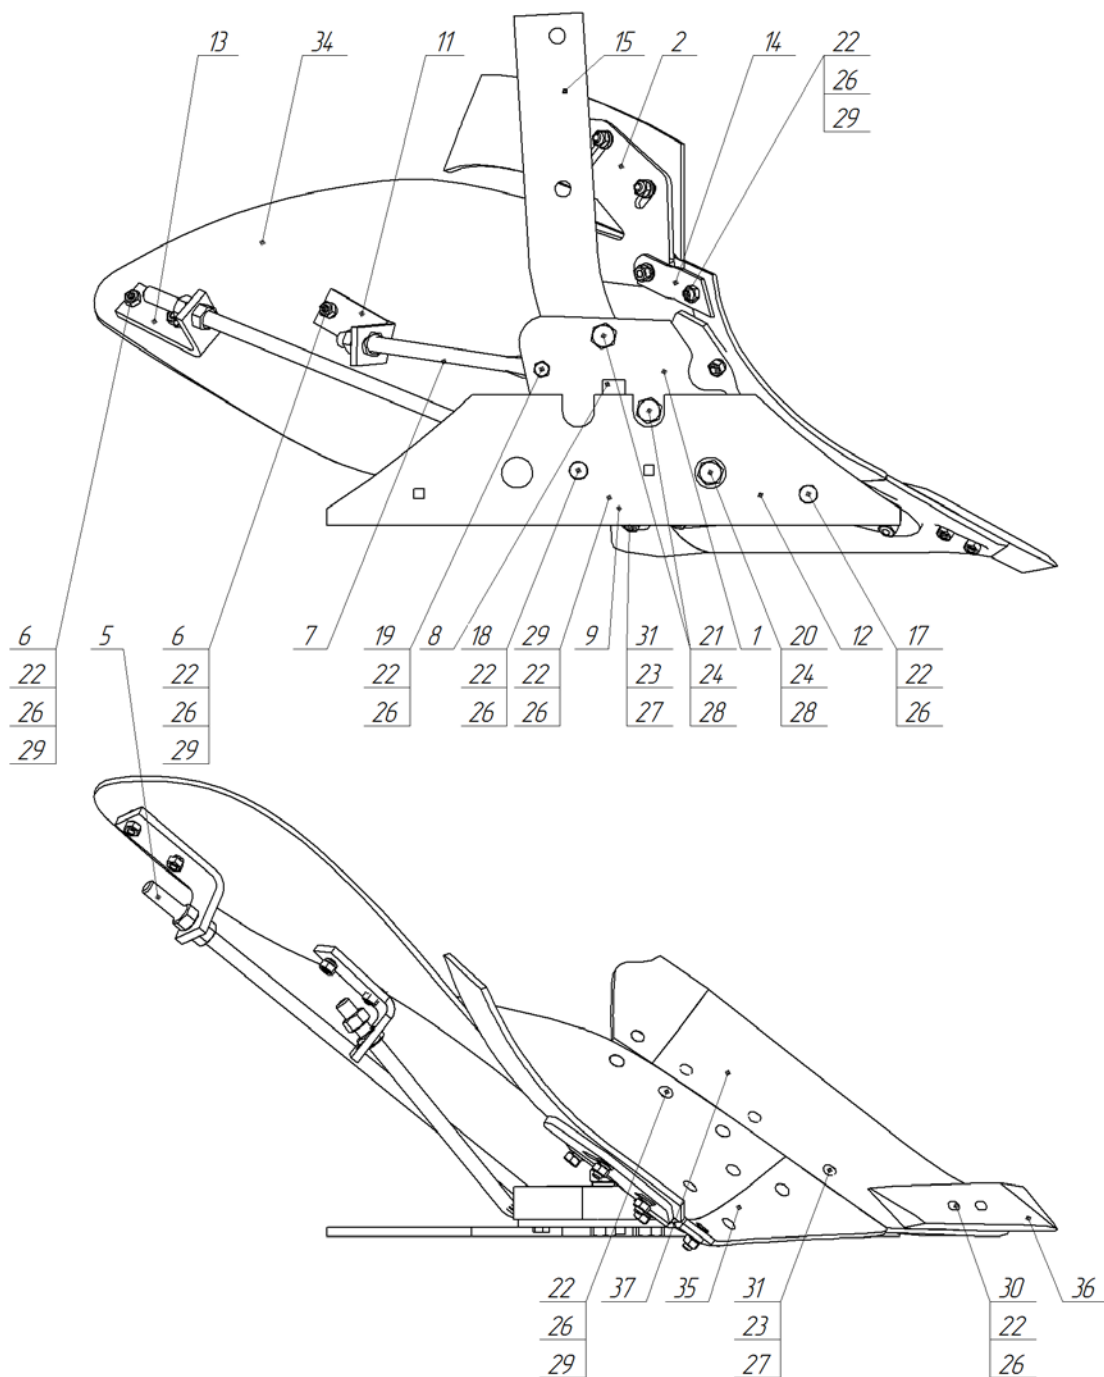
КСО-45 00.00.000-01 Корпус в сборе левый
